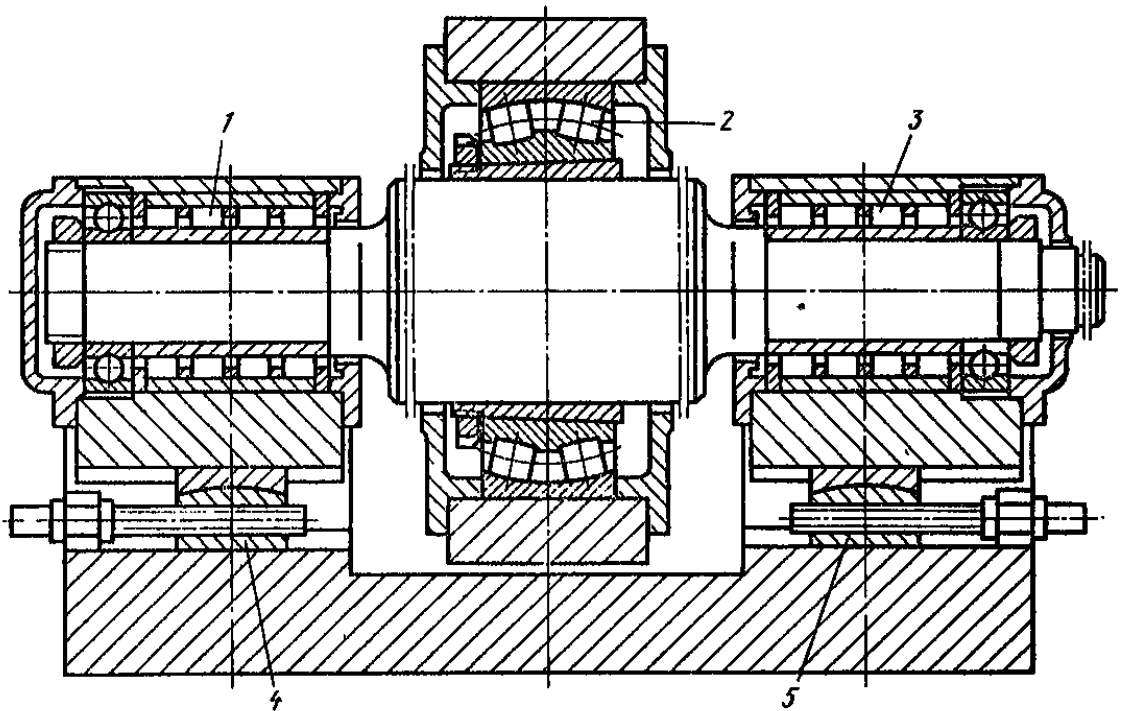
Стенд конструкції ВНІМЕТМАШ для випробування підшипників валкових опор
